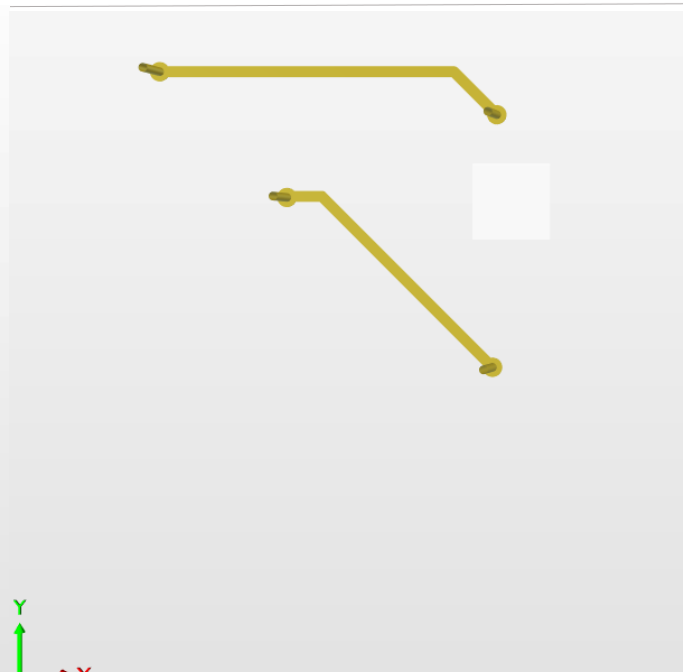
Vederea 3D a PCB-ului (Bottom)
